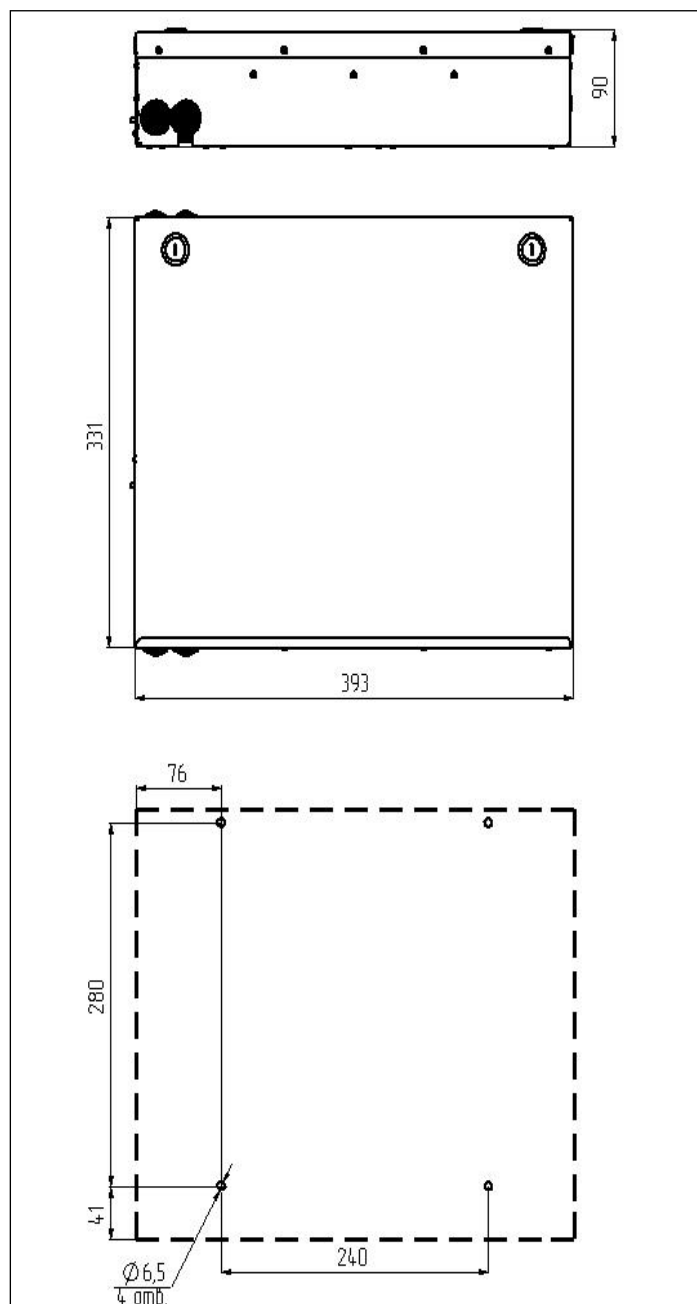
Габаритные и установочные размеры шкафа
